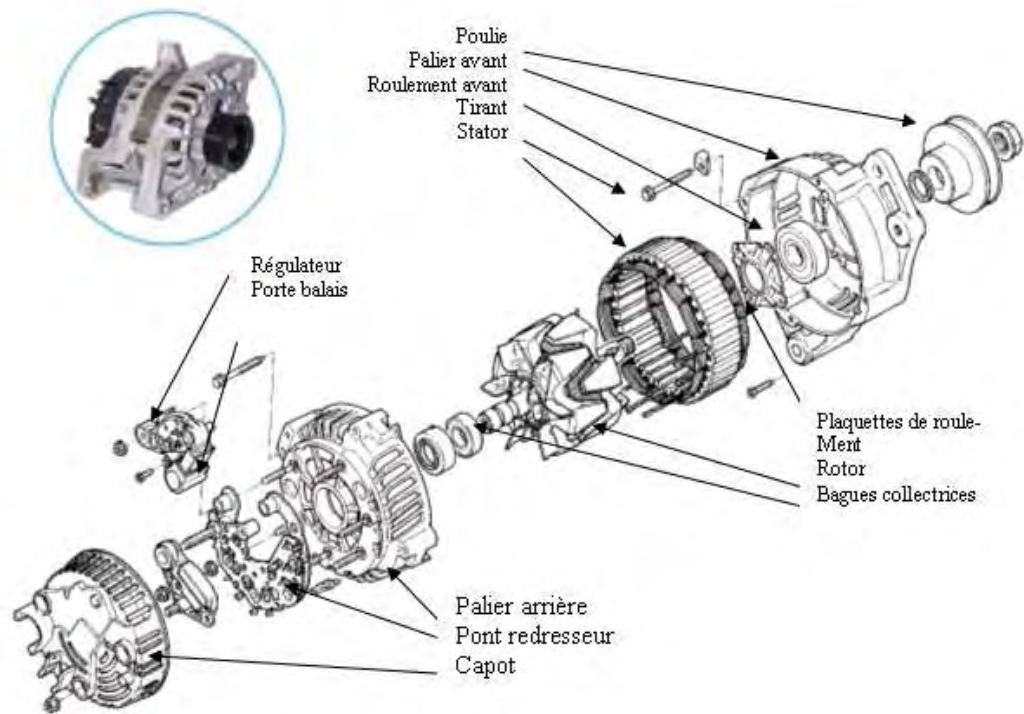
Vue éclatée d'un alternateur à griffes
